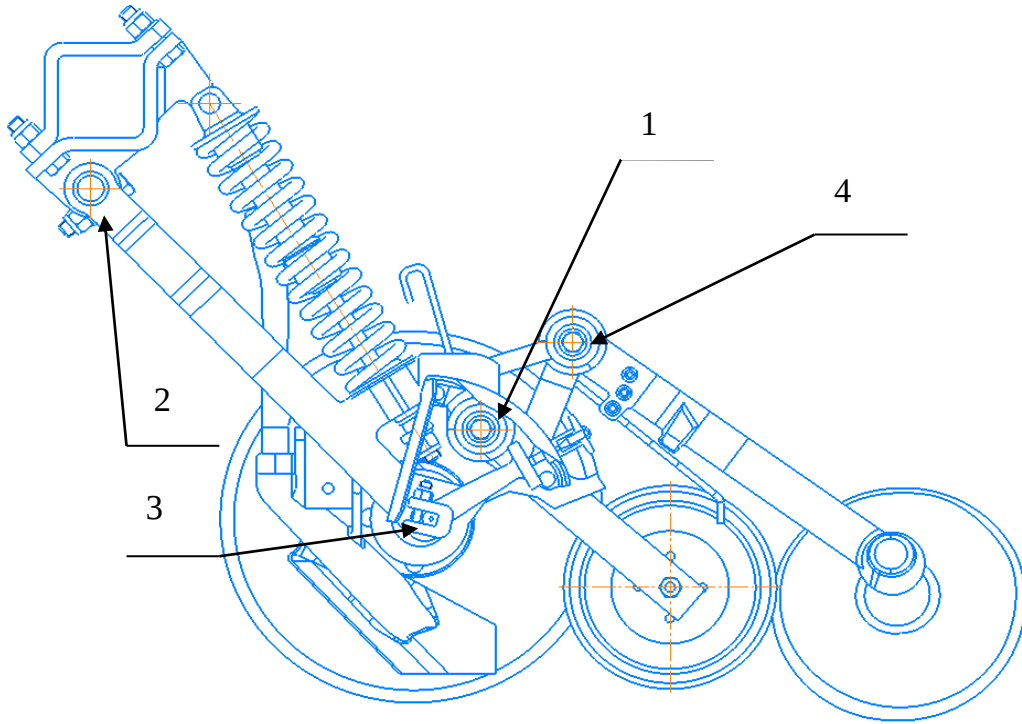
Сошник John Deere серії 90 з проблемними рухомими з'єднаннями: 1 – вузол обертання важеля притискного колеса; 2 – рухоме з'єднання рами посівної секції; 3 – підшипниковий вузол диска сошника; 4 – рухоме з'єднання механізму прикочування.
